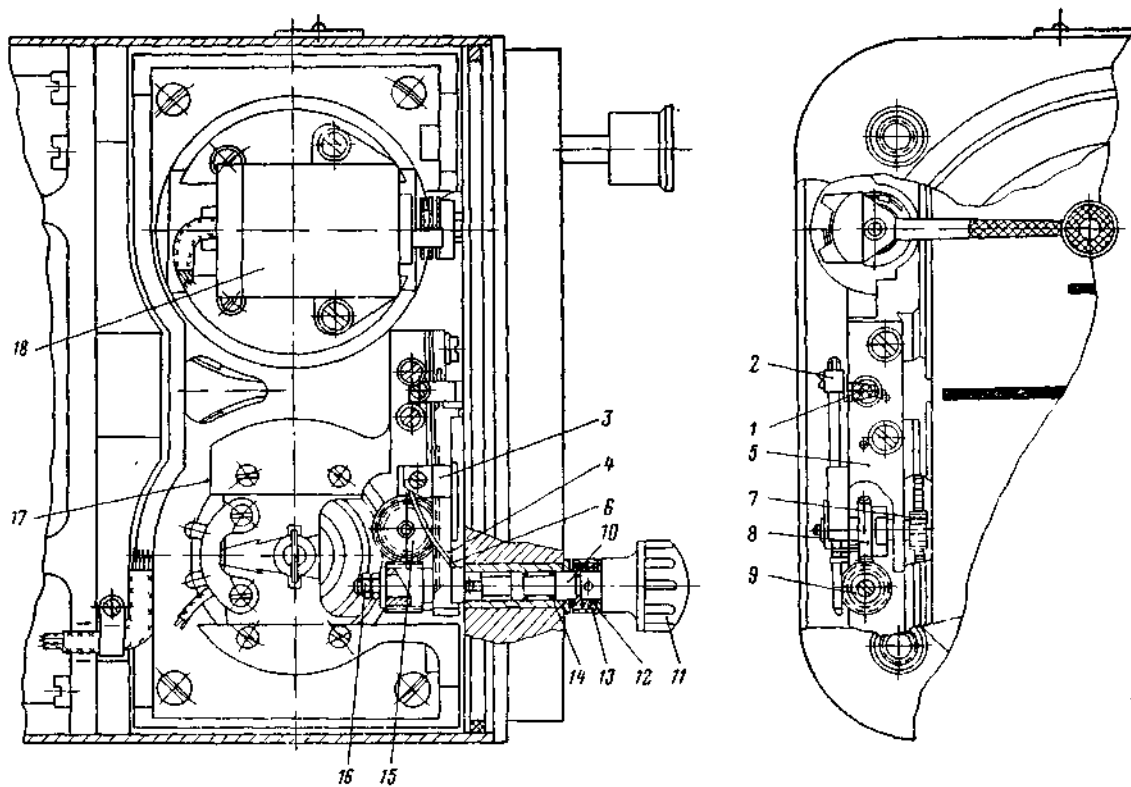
Вид на механизм центровки шкалы тангажа и сигнализатора отказа питания:
